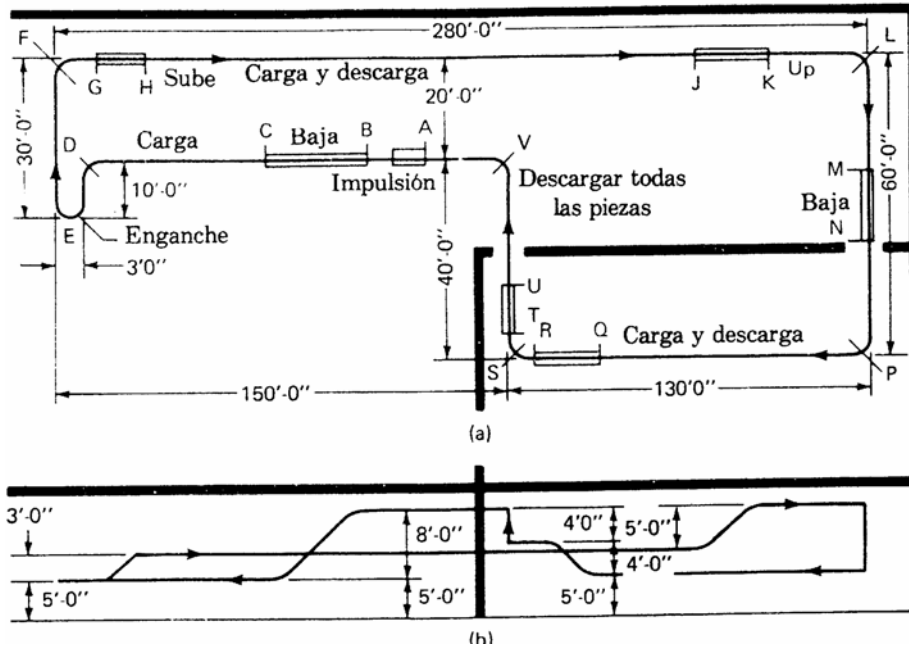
Vista en planta y elevación vertical para sistemas de transportador con carros.
